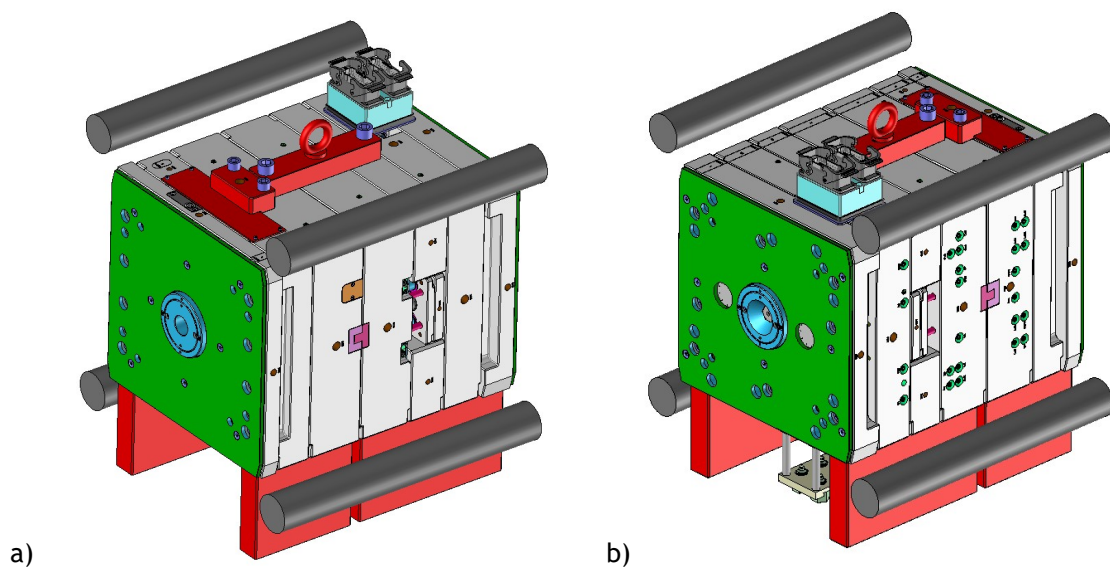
3D final com simulação do molde nas colunas da máquina de injeção. a) Vista do molde do lado do operador. b) Vista do molde do lado oposto ao operador.
